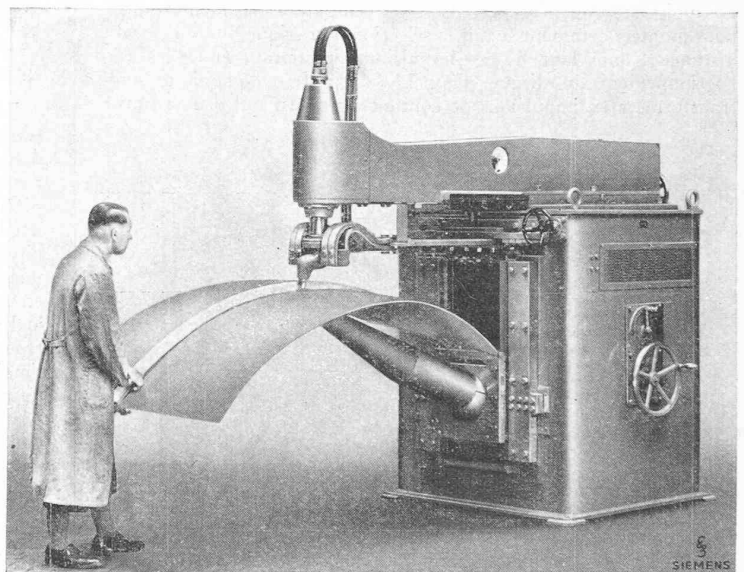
Parmi les procédés modernes du travail des métaux, la soudure électrique acquiert une importance toujours croissante. Les nouvelles machines à souder par résistance ont une puissance continue pouvant aller jusqu'à 150 kVA et une saillie de 500 à 1200 mm.
